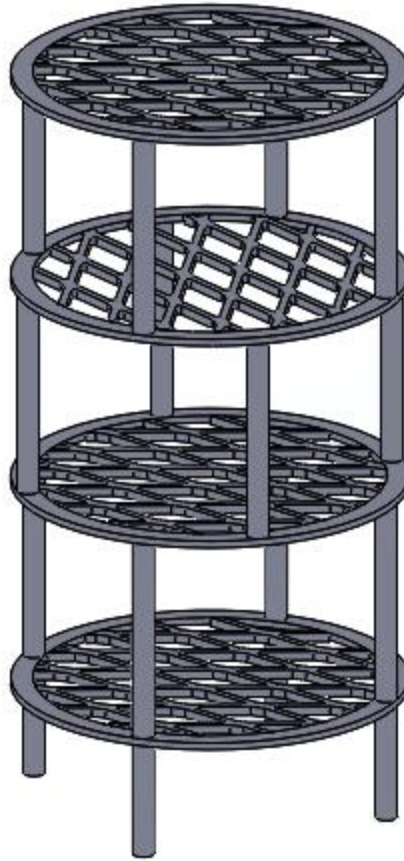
Acoplamiento de las parrillas para formar la cesta de trabajo donde se montan las piezas a nitrurar.
